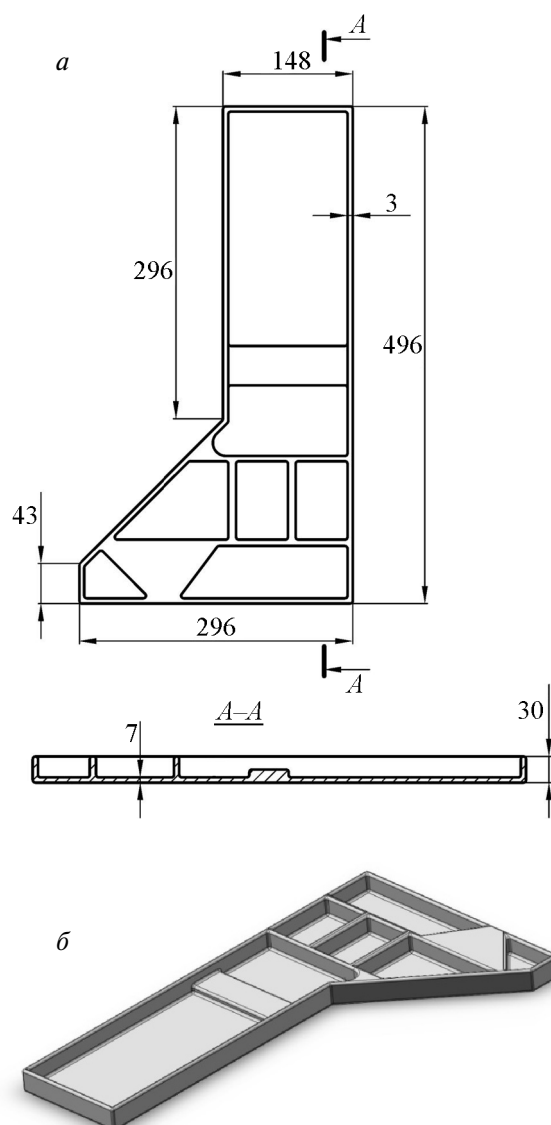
Чертеж детали «стойка» (а) и трехмерная модель штампованной поковки для этой детали (б)
